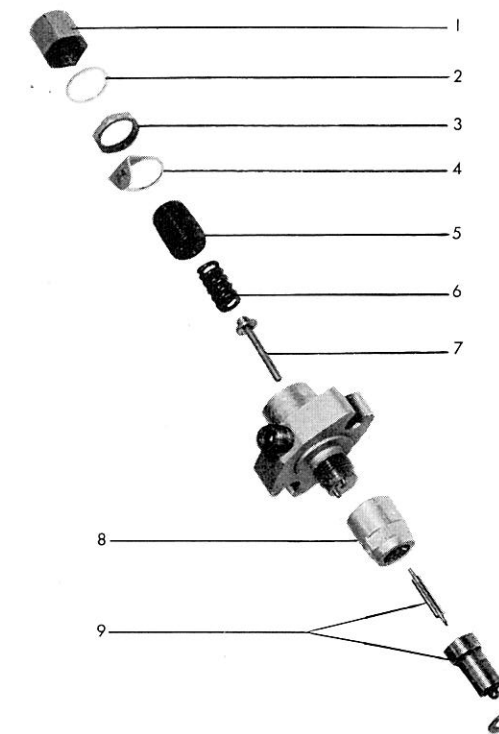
Ordre de démontage de l'ensemble injecteur porte-injecteur
